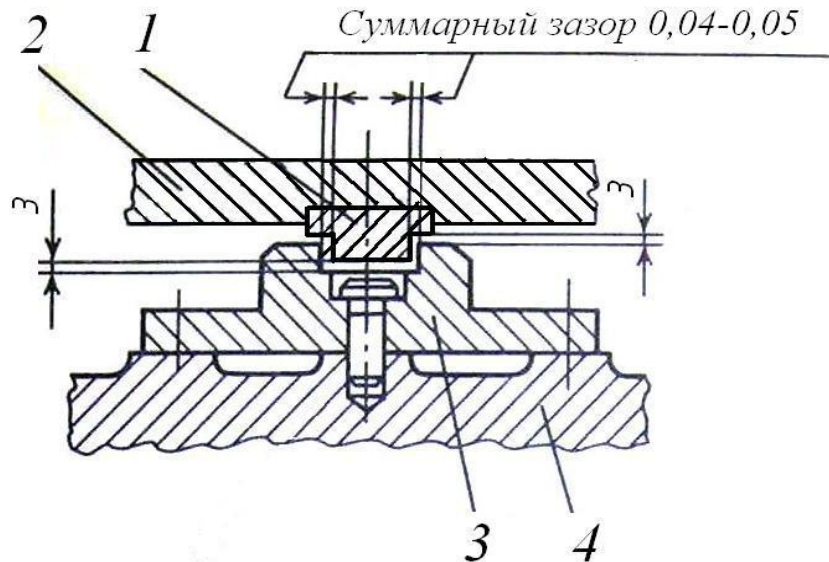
Опираие корпусов ЦВД турбин ХТЗ на корпус подшипника [9]
